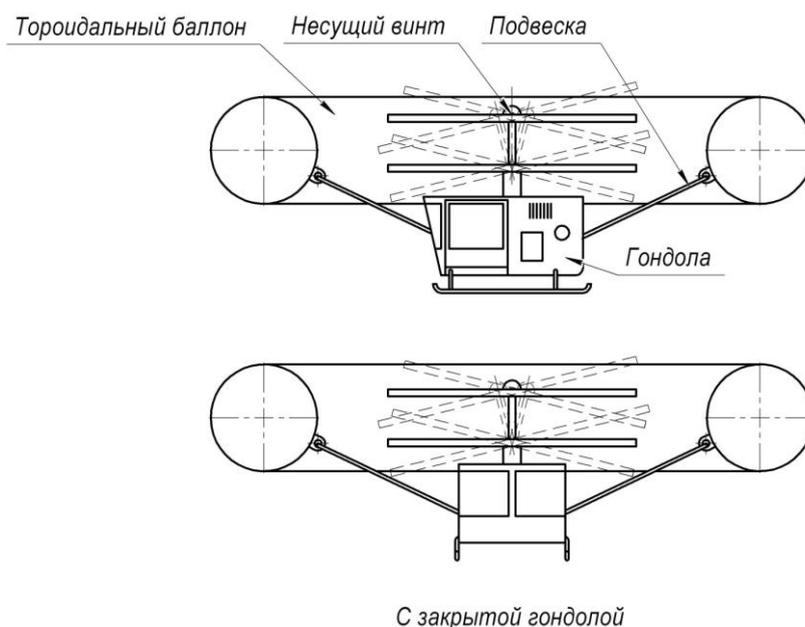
Предлагаемый одноторный торокоптер: устройство (компоновочная схема) и схема работы
